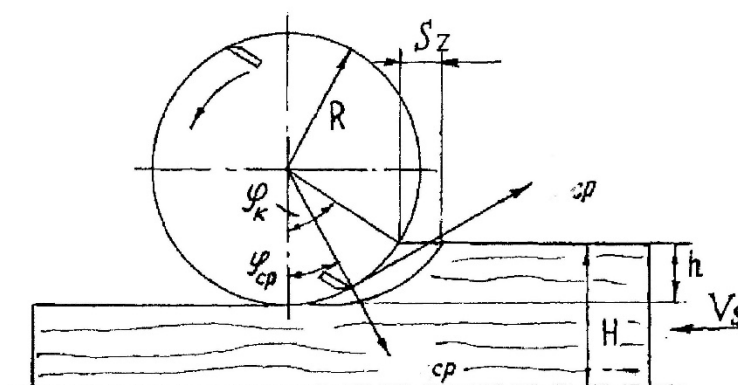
Зусилля різання та геометрія ріжучого шару при циліндричному фрезеруванні
